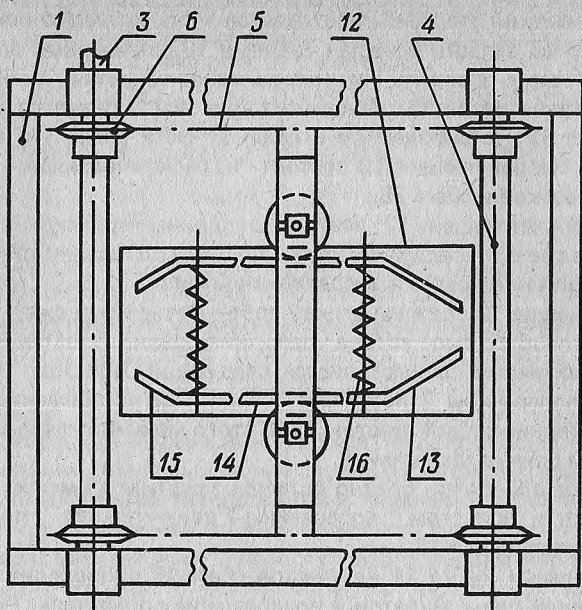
Общая схема механизма центрирования и подачи фрезерно-брусующей машины.
